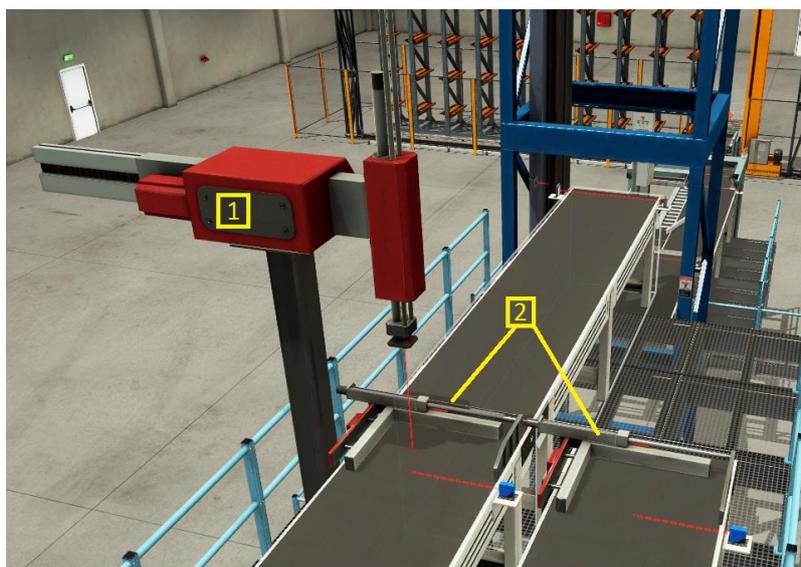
, Elaboración Propia, Montaje. 1. Brazo de Montaje / 2. Bridas de colocación y barreras
